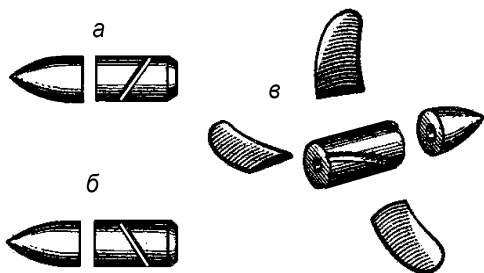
Виготовлення паяного гребного гвинта:
